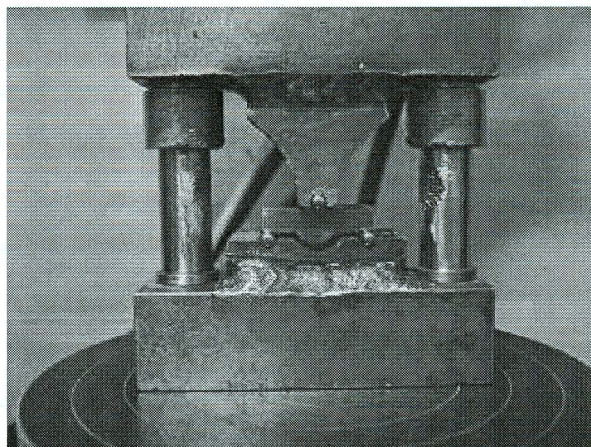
Dispositivo para ensaio de TRS – Norma ASTM B 528-99.
